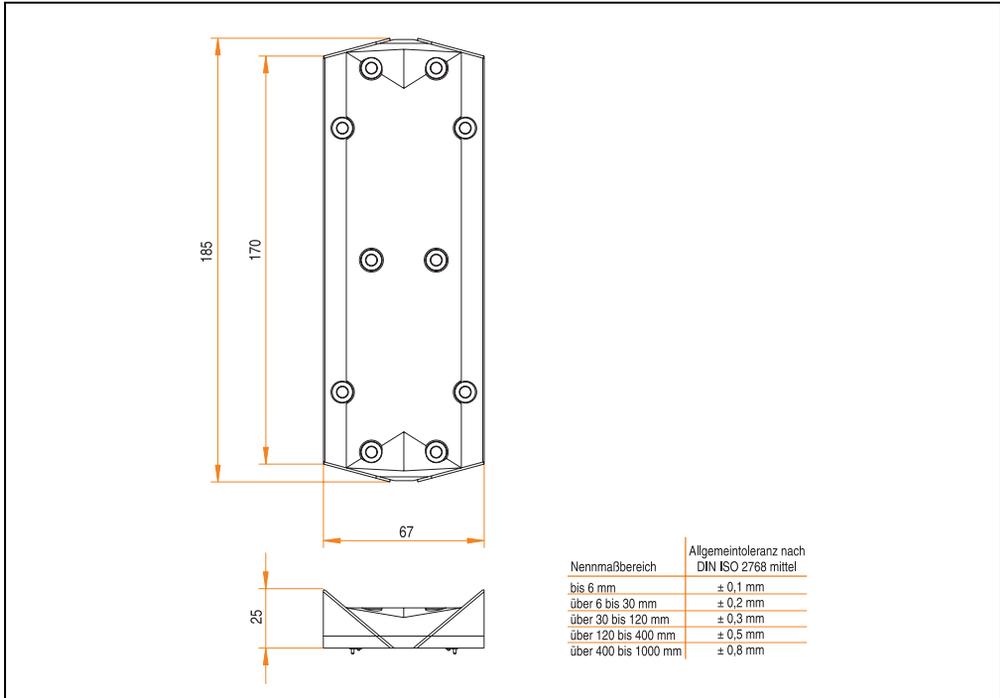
Abmessungen Extension Connector 5AC800.CON1-00
